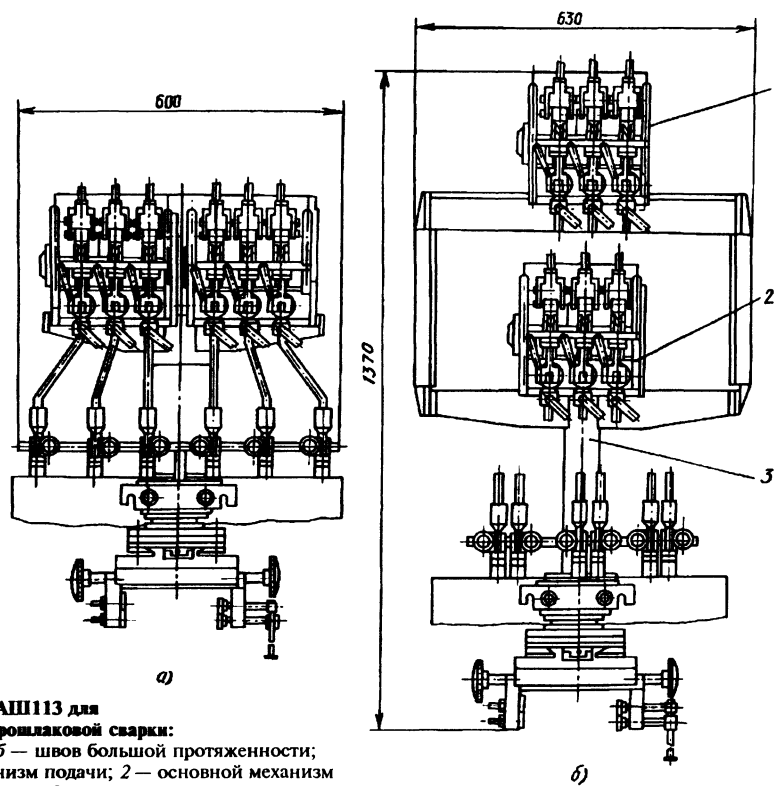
Автомат АШ113 для электрошлаковой сварки:
